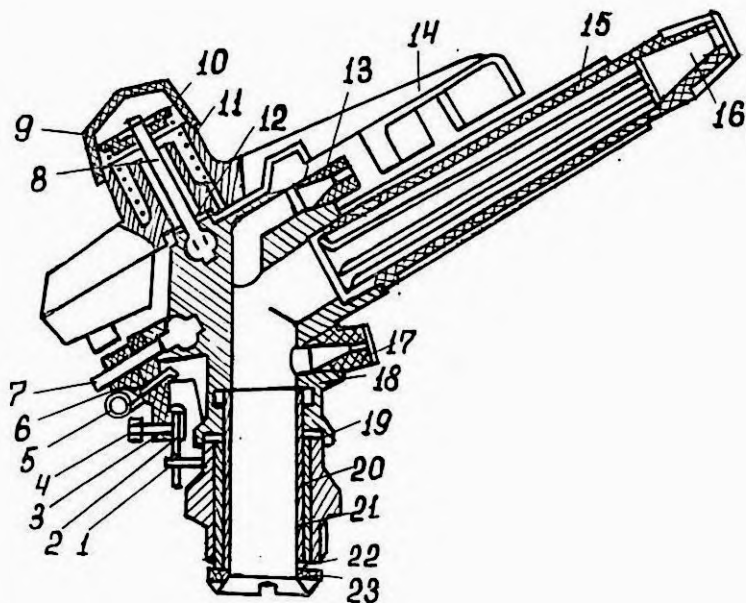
Среднеструйный дождевальный аппарат «Роса-3»: 1 — стопорное кольцо; 2 — стержень; 3 — рычаг; 4 — винт; 5 — пружина; 6 — упор; 7, 8 — ось; 9 — колпачок; 10 — фиксатор; 11 — возвратная пружина; 12 — шайба; 13, 17 — вспомогательные сопла; 14 — коромысло; 15 — ствол; 16 — основное сопло; 18 — корпус; 19 — основание; 20 — втулка; 21 — стакан; 22 — фторопластовая шайба; 23 — резиновая шайба.
